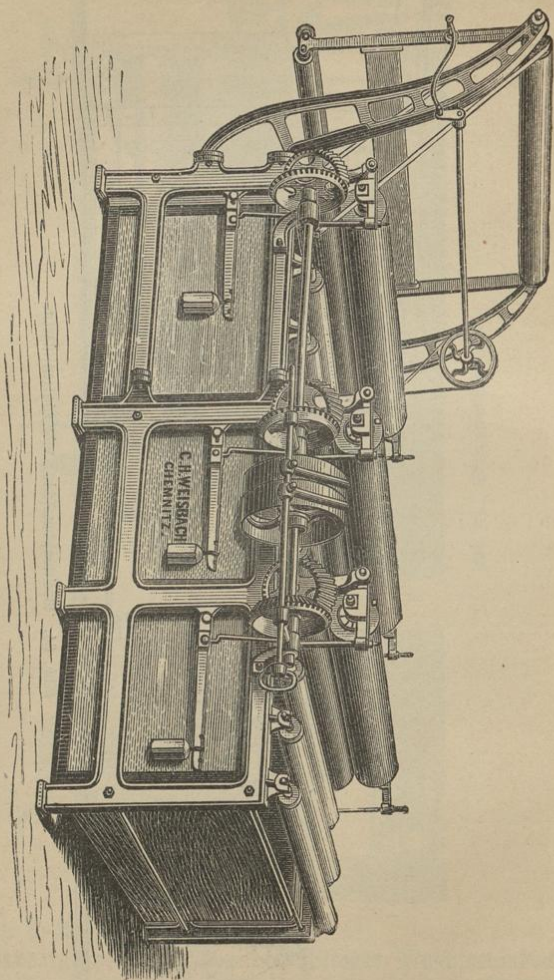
Breitwalzmaschine mit Walzenflügeln.
